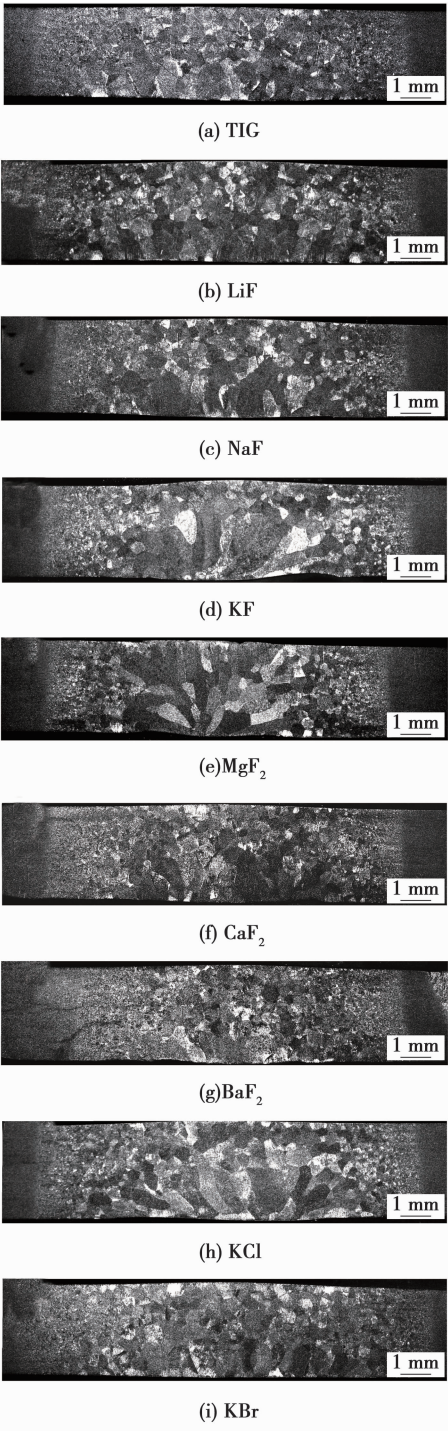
TIG 和 ATIG 焊焊缝宏观组织形貌
